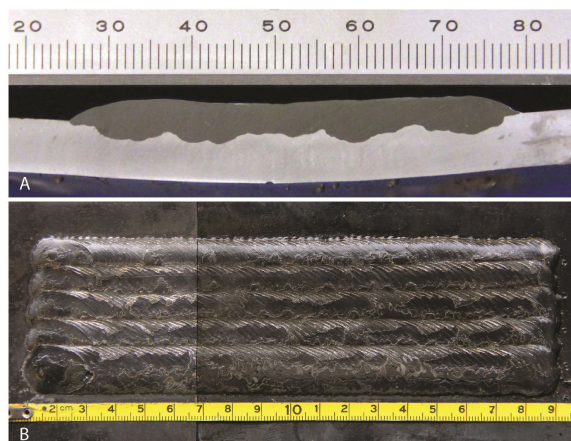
Resultado do procedimento de revestimento: A – seção transversal, B – cordões de solda
